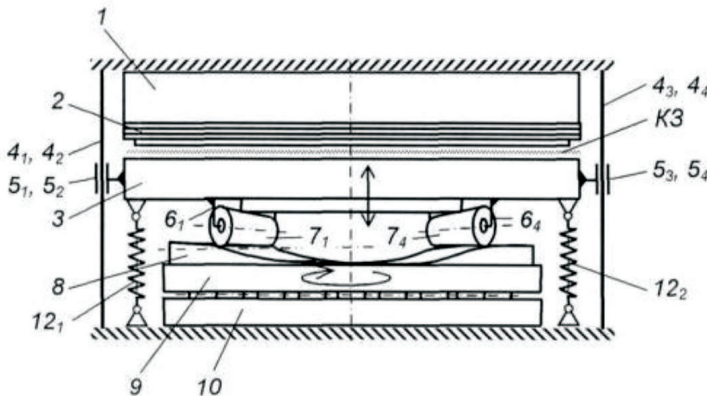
Плоский штанцювальний прес з роликовим механізмом привода натискної плити
